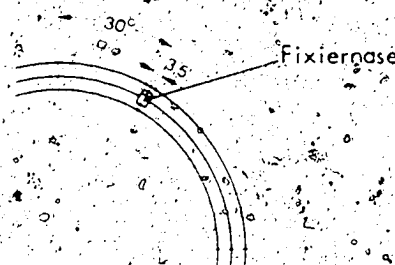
Fixiernase 3,5 mm (neue Ausführung)
